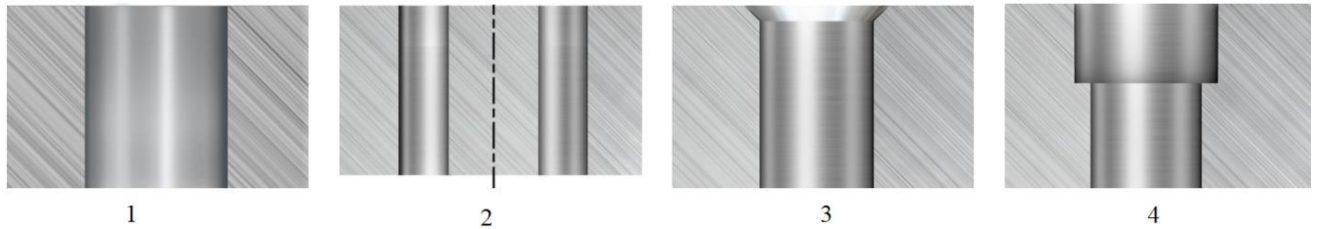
Методи свердління отворів: 1 – звичайне свердління; 2 – трепанування (свердління корончастим свердлом); 3 – з фаскою; 4 – ступінчасте свердління
